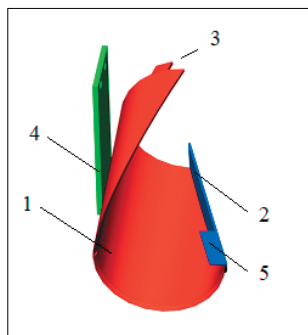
Схема рабочего органа для прецизионной обработки почвы: 1 – усеченный цилиндрический отвал; 2 – направляющая доска; 3 – сталкиватель; 4 – стойка; 5 – крыло
